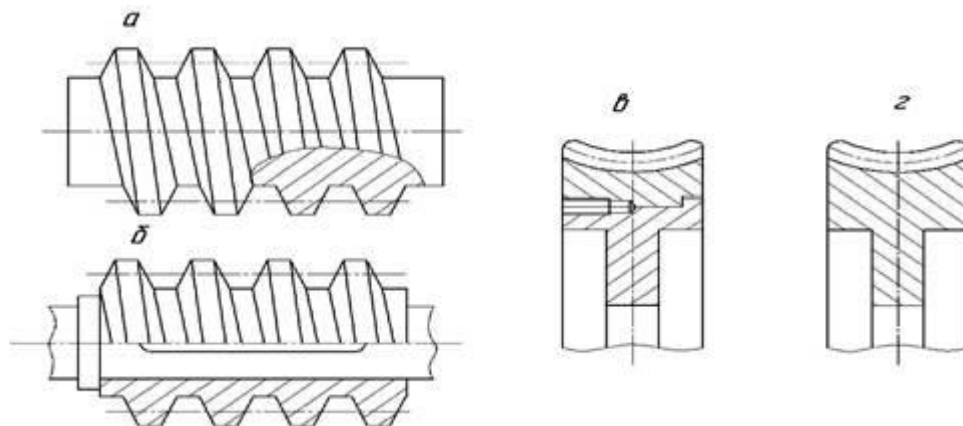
Конструктивні схеми черв'яка і черв'ячного колеса
